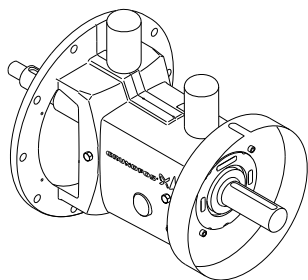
Кронштейн подшипника с автоматическими маслёнками для консистентной смазки
